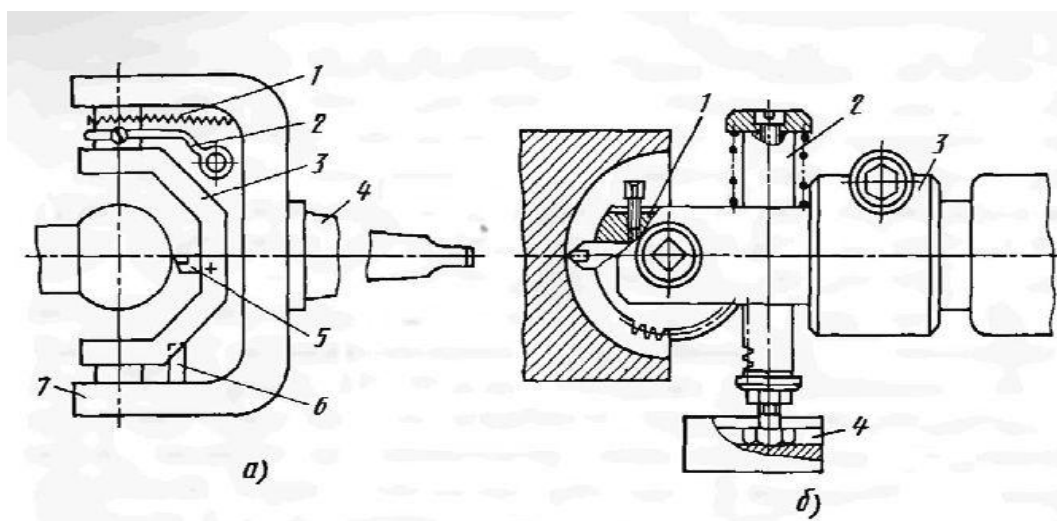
Приспособление, установленное в пиноли задней бабки (а)
